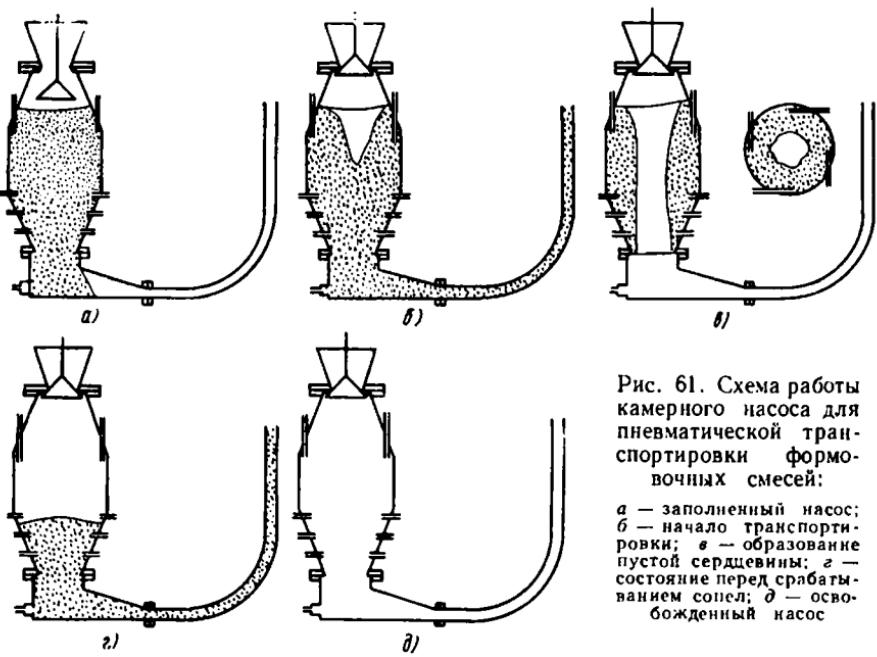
Схема работы камерного насоса для пневматической транспортировки формовочных смесей:
